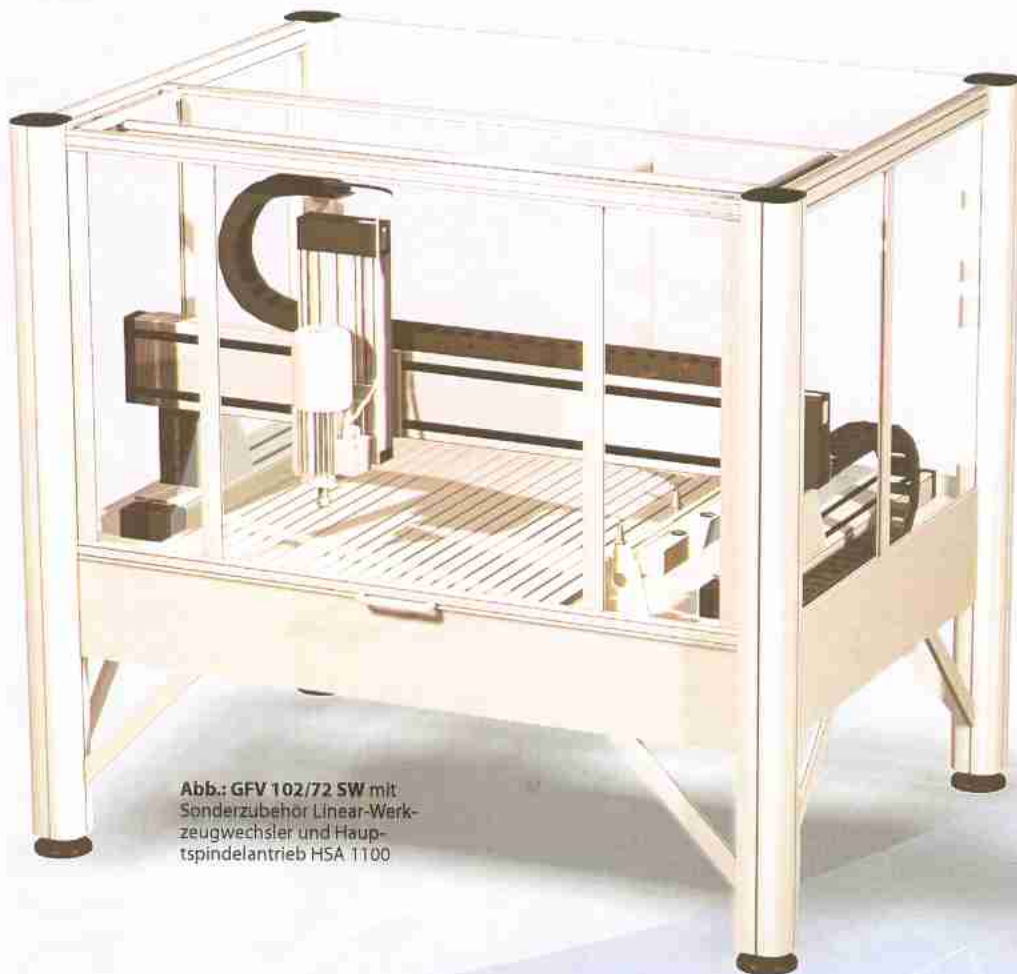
/72 SW mit Sonderzubehör Linear-Werkzeugwechsler und Hauptspindeltrieb HSA 1100
